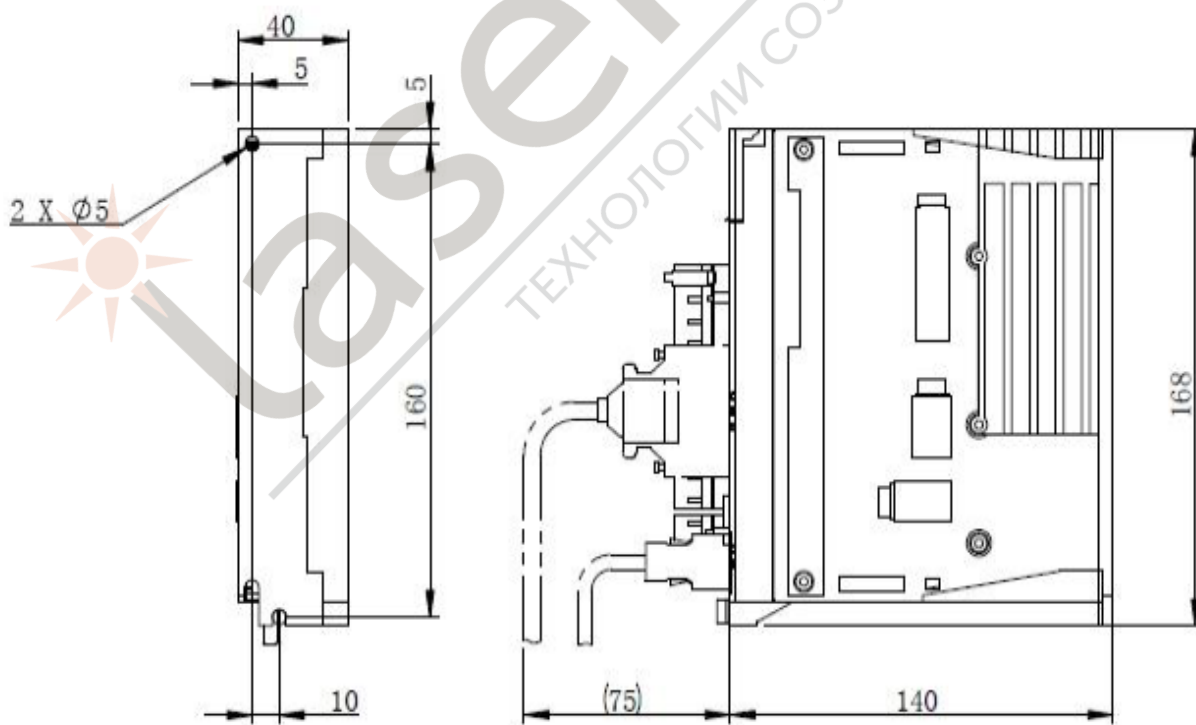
Габаритные размеры серводвигателя (мм)
